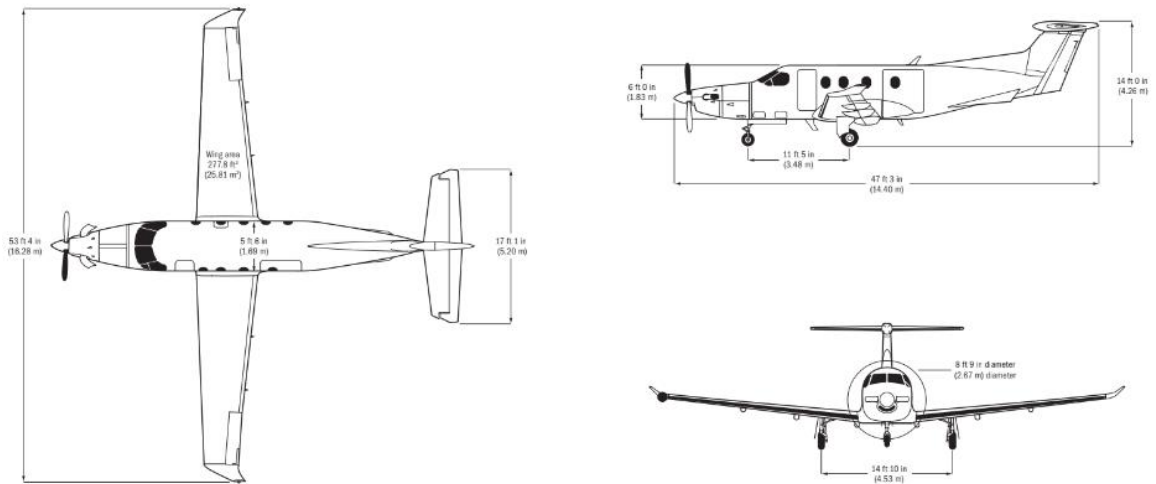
Planta, perfil y alzado del Pilatus PC-12 NG [6]
